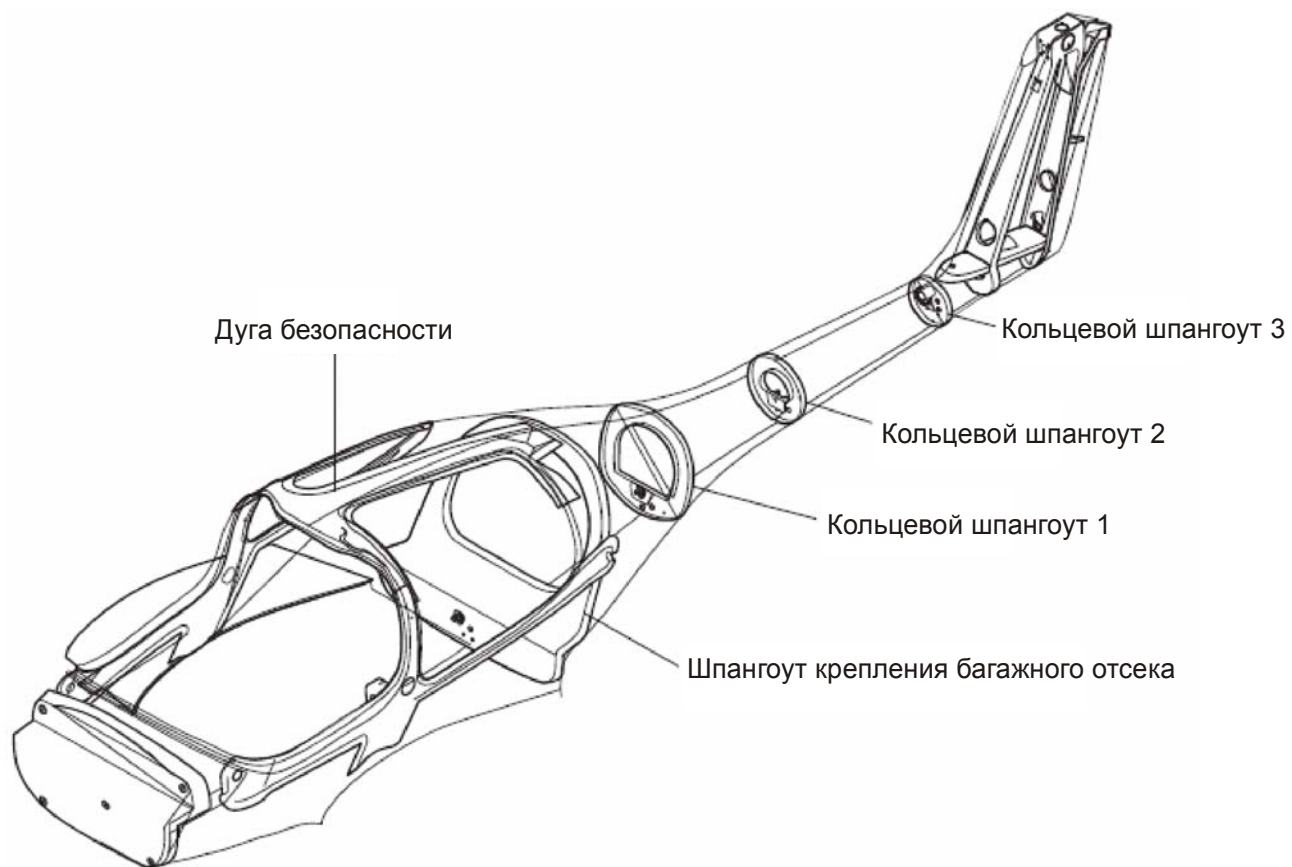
Конструкция фюзеляжа (хвостовая часть)
